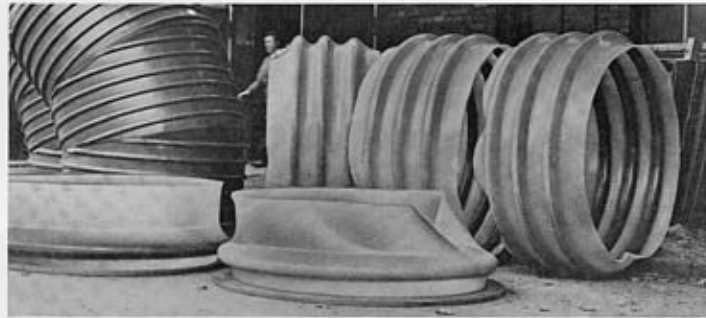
Dreiwellige Kompensatoren vor dem Einbau
